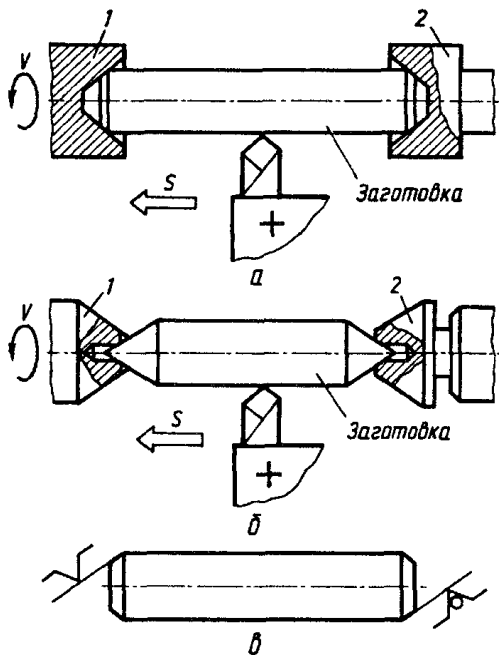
Закріплення заготовки в обертових центрах (тертьових повідках):
